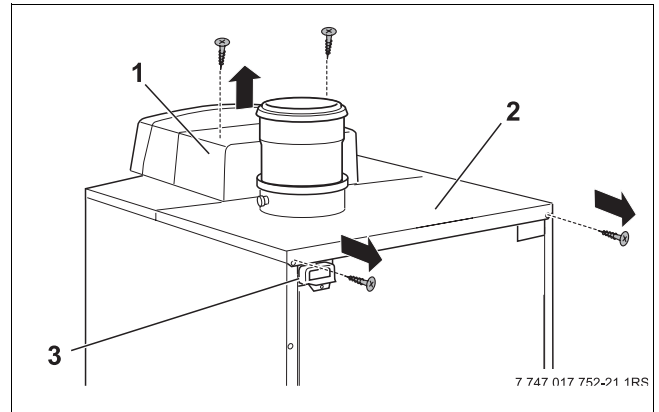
Retirer le couvercle et le capot arrière de la chaudière
